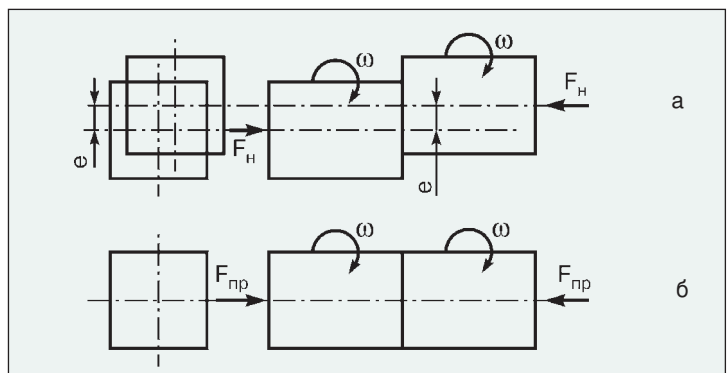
Схема вибрационной СТ: а — колебательные движения одной свариваемой детали относительно другой; б — колебательные движения одной свариваемой детали с вращением
